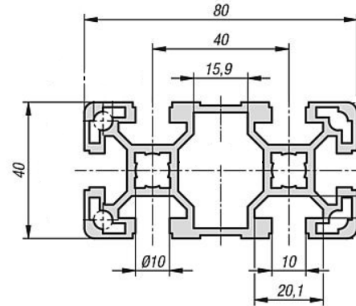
Dimensiones de perfil de aluminio 80mmx40mm.
